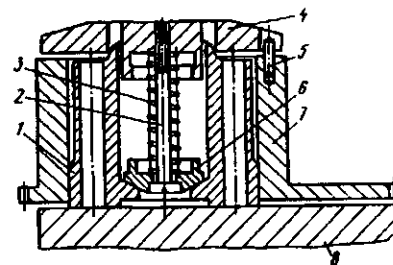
Кассета для доводки плоской поверхности на станке с планетарным механизмом: 1 – деталь; 2 – винт нагрузочного устройства; 3 – пружина; 4 – фланец; 5 – штифт; 6 – прижимная втулка; 7 – специальная кассета; 8 – притир
